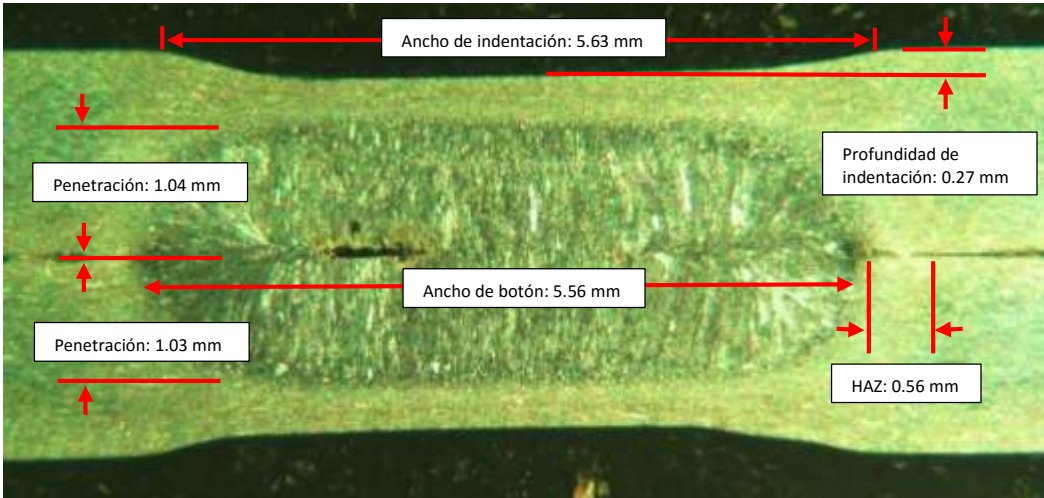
Mediciones realizadas en el botón de soldadura número 16.
